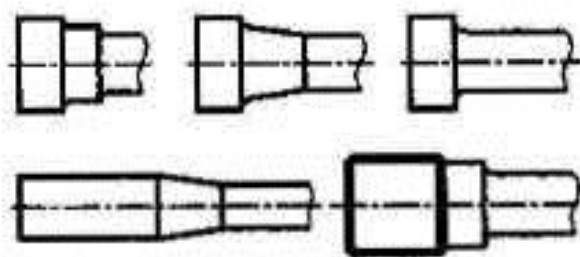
Типы головок цилиндрических образцов для испытаний на растяжение
